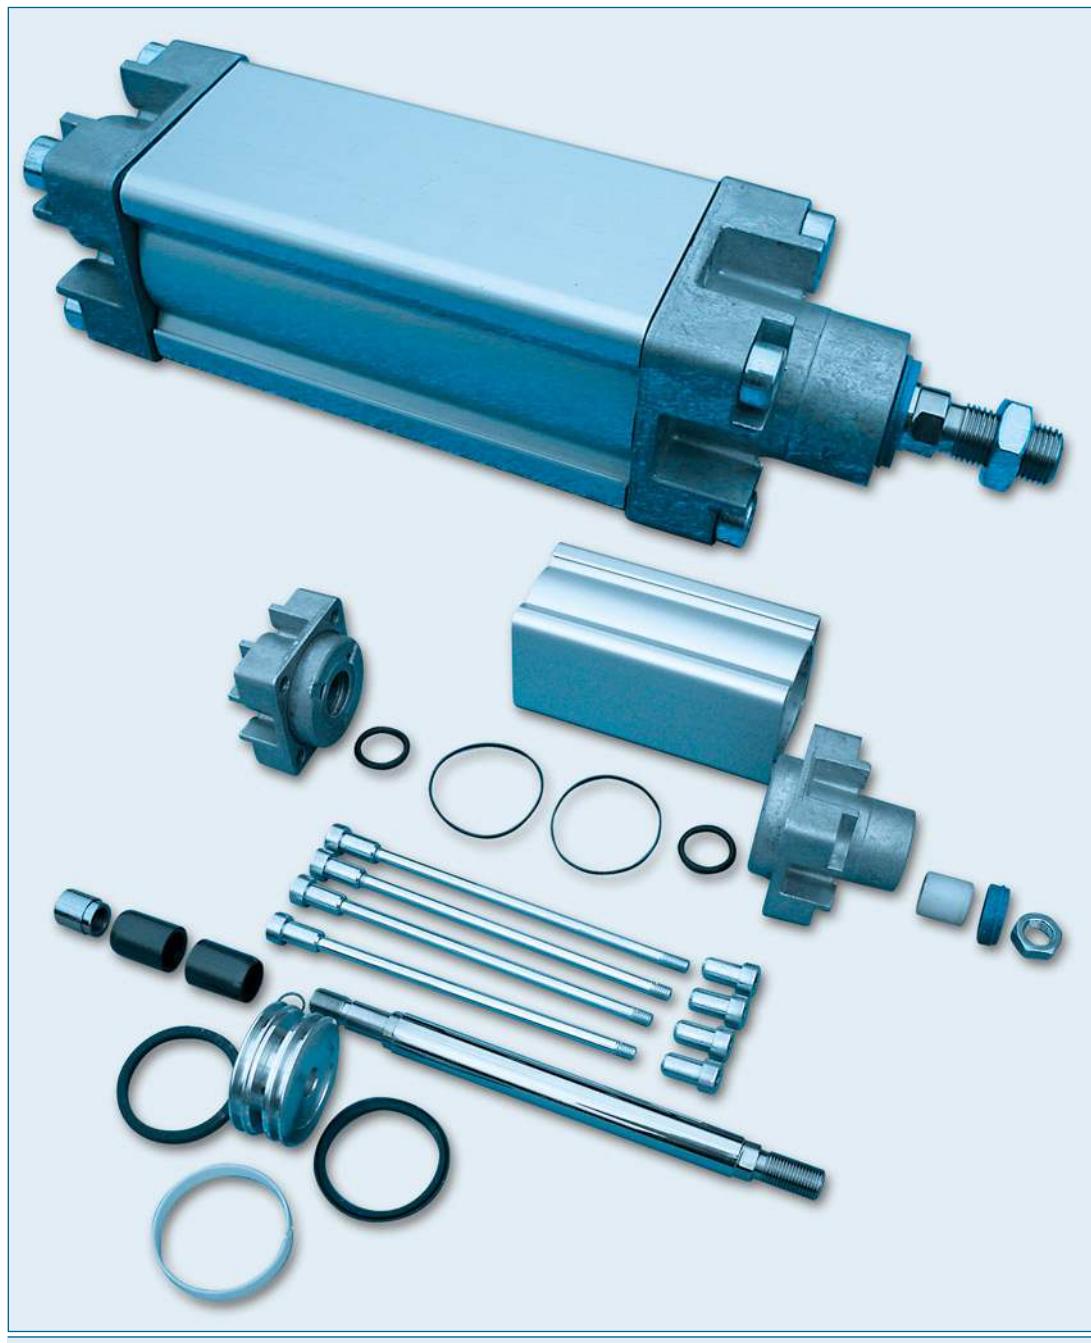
Pneumatikzylinder – zusammengesetzt aus Einzelteilen und Baugruppen
